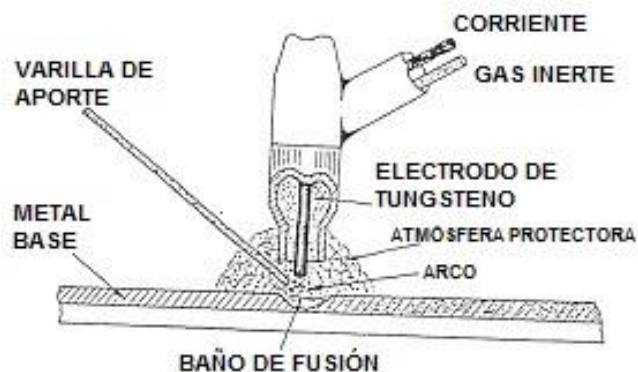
Soldadura TIG (Fuente: Escuela de soldadores)
